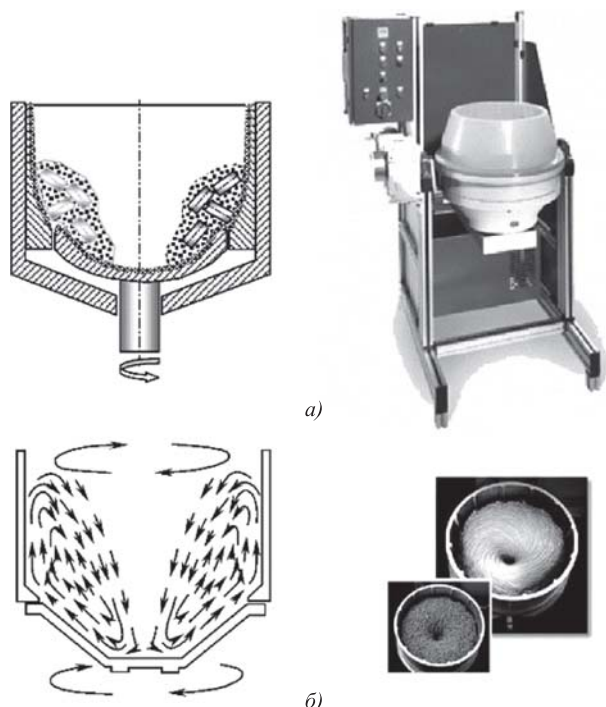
Схемы установок для центробежно-ротационной обработки со сферической (а) и конической тарелью (б)
